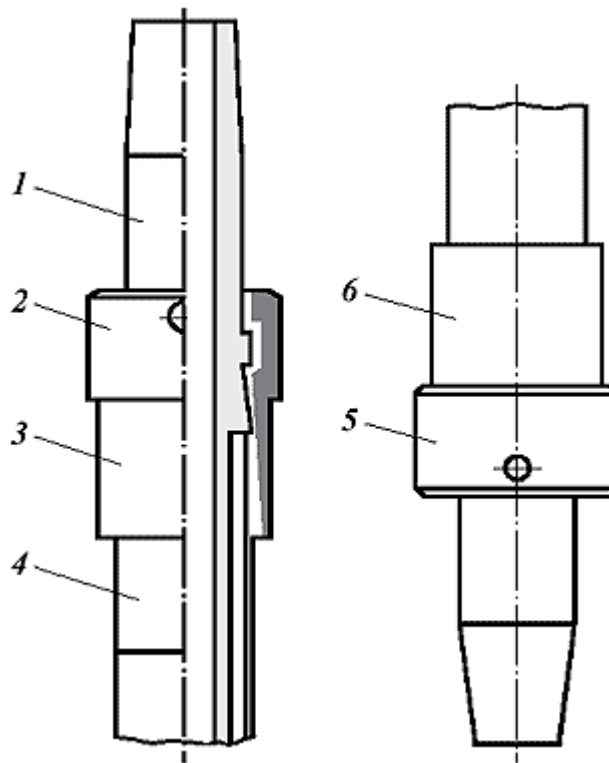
Пакер заколонный типа ПЗ-168Ц: 1 – ствол; 2, 6 – гайки верхняя и нижняя; 3, 5 – корпус; 4 – цилиндрическая гильза
